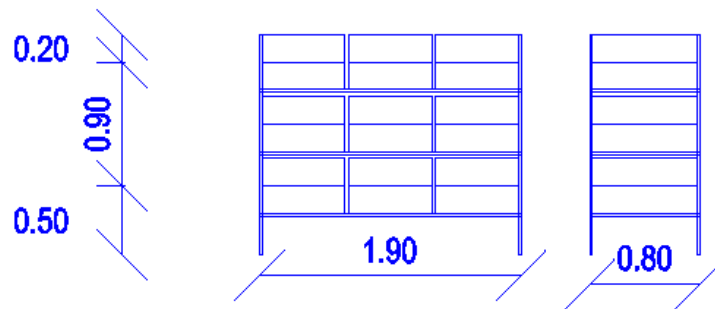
Vista frontal e vista lateral da rack standard supermercado
